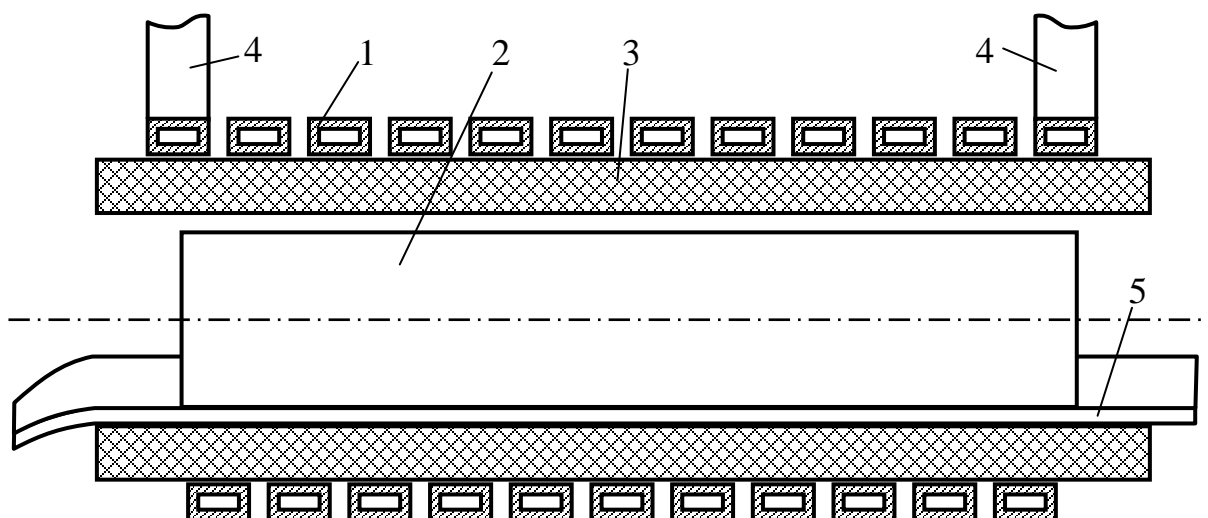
Система индуктор–заготовка (1 — многовитковый индуктор с электрической изоляцией, 2 — заготовка, 3 — тепловая изоляция, 4 — токоподводы, 5 — направляющая)
